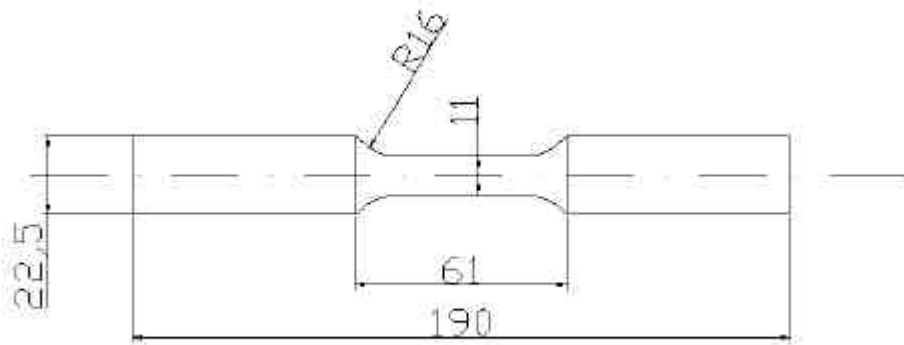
Desenho com as dimensões do corpo-de-prova após a usinagem.
